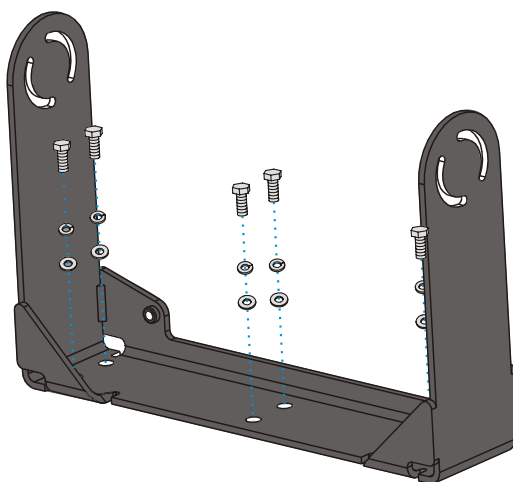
Befestigung des unteren Montagewinkels am Fahrzeug
